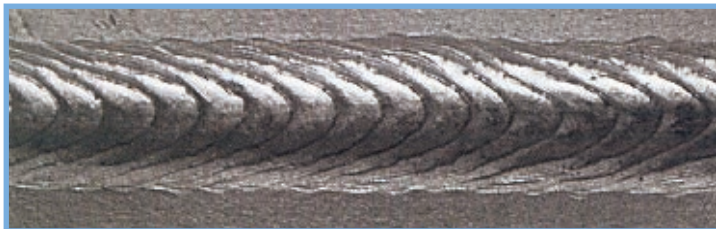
Вид шва, выполненного автоматической TIG-сваркой
